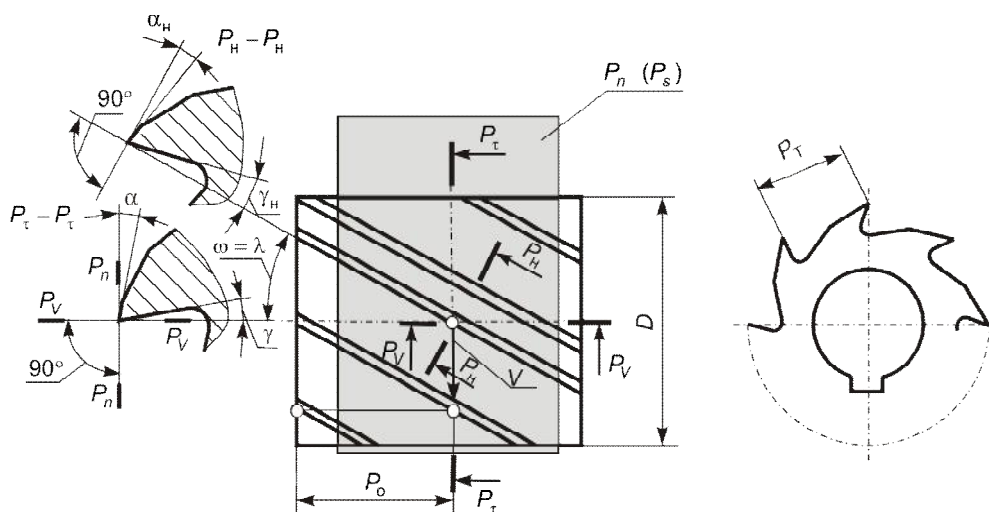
Геометрические параметры режущей части цилиндрической фрезы
